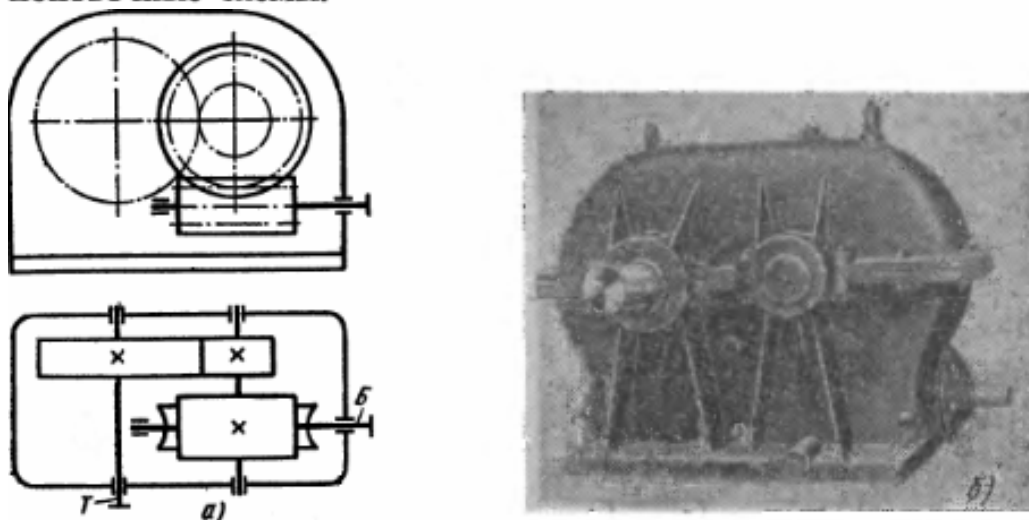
Червячно-цилиндрический двухступенчатый редуктор:
